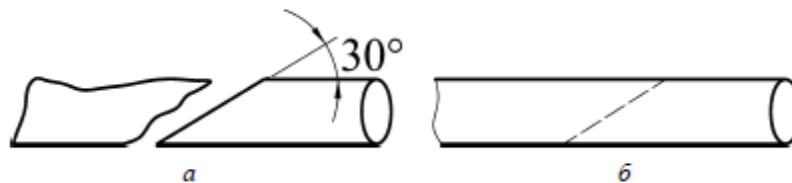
Схема кузнечной сварки: а – до сварки; б – после сварки
